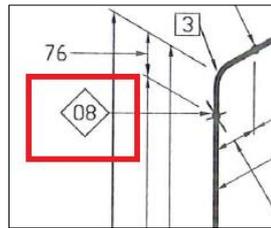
Soldadura de taller.
